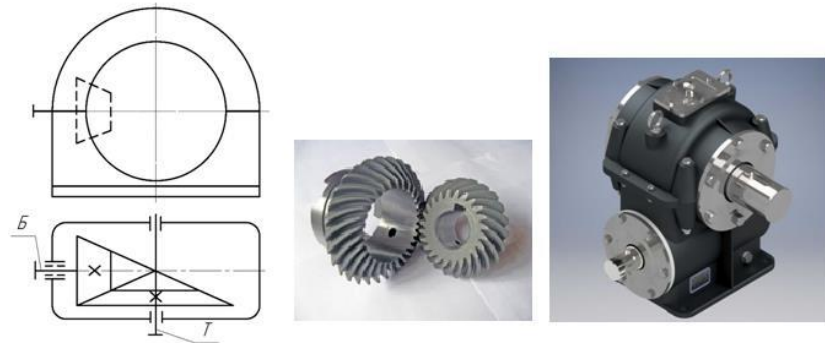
Одноступенчатый редуктор с коническими зубчатыми колесами
